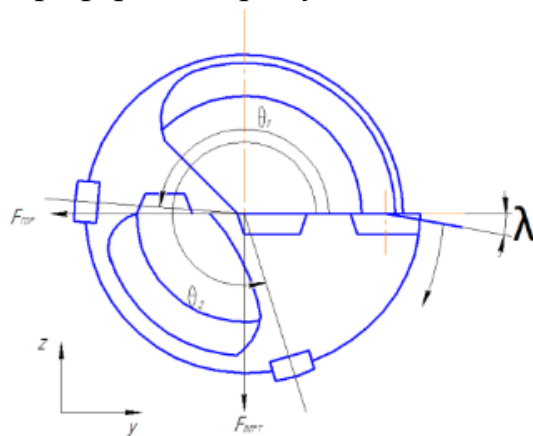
Поворот периферийной режущей пластины на  $-10^\circ$
